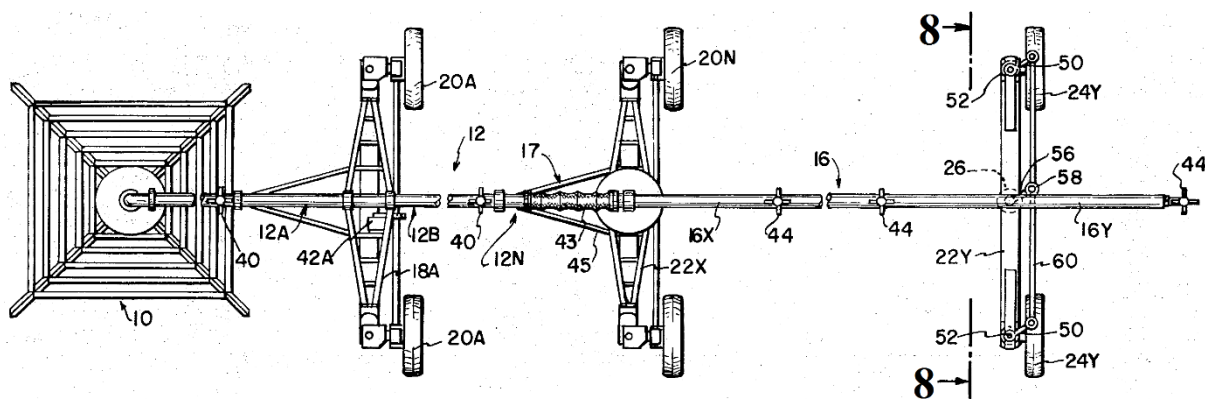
Vue en plan d'ensemble bras principal et bras d'extension [9].
